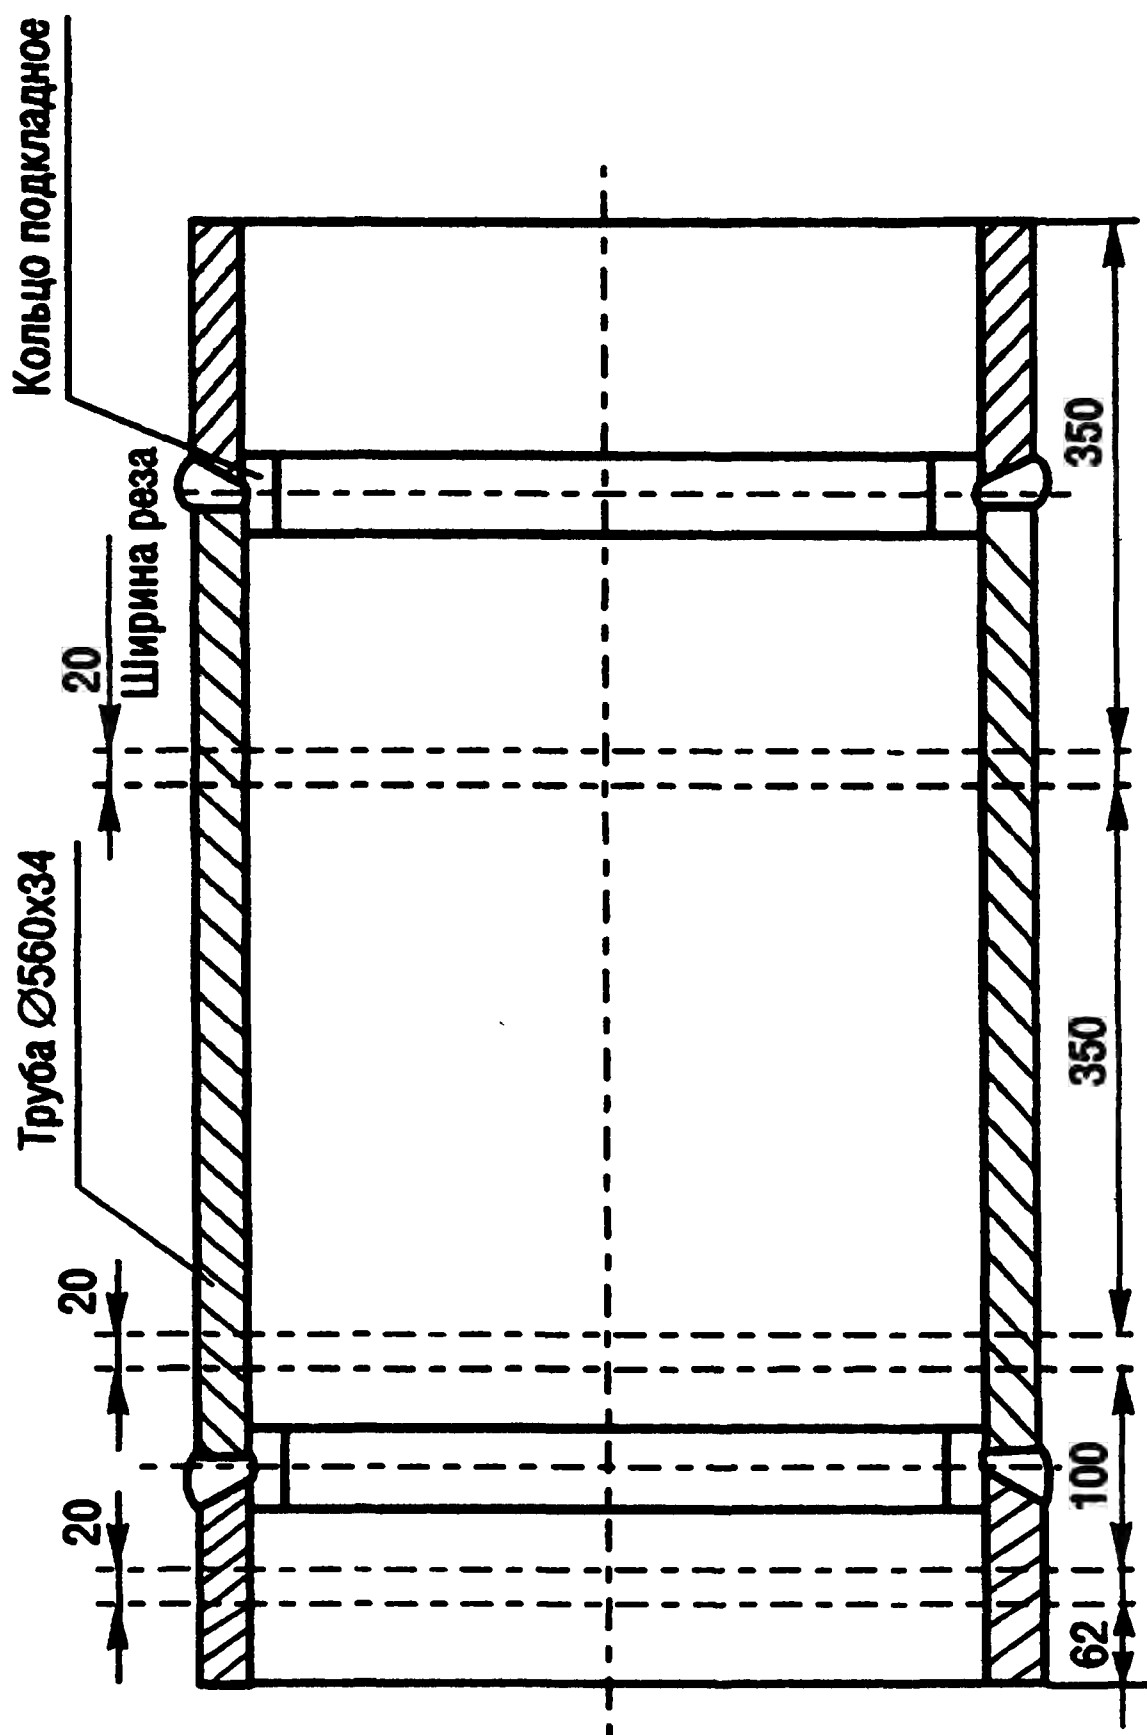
Схема сварки трубы и резки на заготовки
